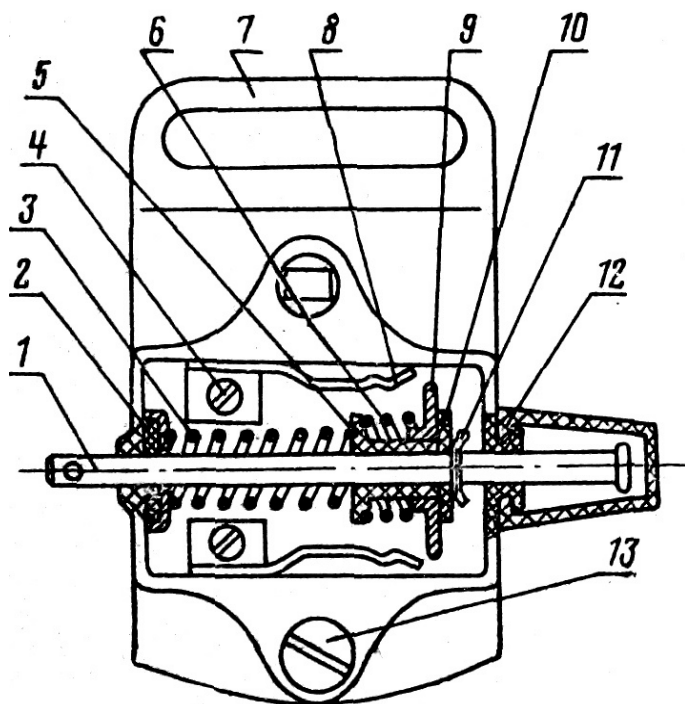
Выключатель стоп-сигнала ВК-854: 1 — шток; 2 — фетровый сальник; 3 — пружина штока; 4 — клемма; 5 — изолирующая втулка; 6 — пружина задержки выключения; 7 — кронштейн; 8 — контактные пластины; 9 — контактная шайба; 10 — изолирующая шайба; 11 — шплит; 12 — резиновый чехол; 13 — винт крепления выключателя к кронштейну
